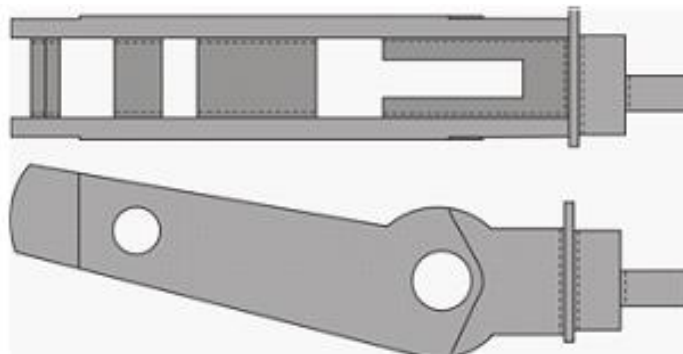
Схема сканирования околошовных зон сварных соединений рычага 4075.42.140 клещевого механизма
